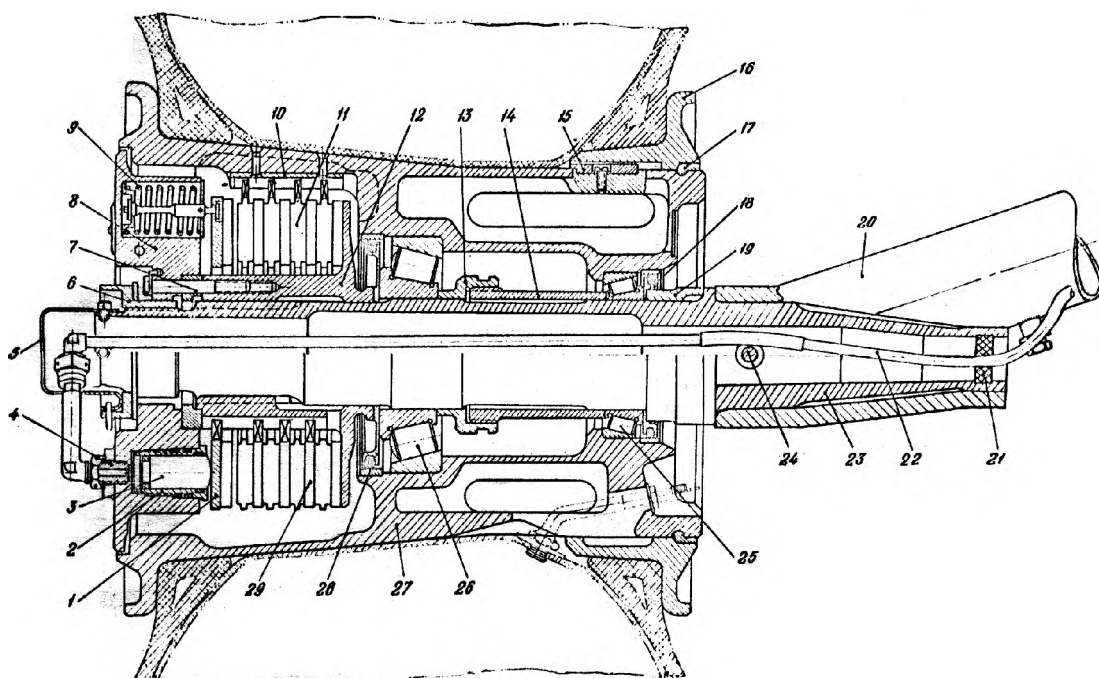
Устройство колеса главной стойки шасси вертолета Ми-24А [13]:
